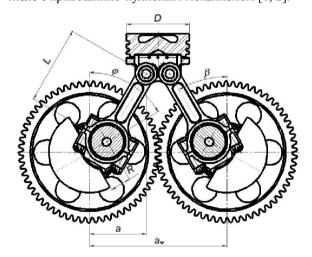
Схема двухвального ДВС с зубчатыми синхронизирующими секторами на поршневых головках шатунов [3]
